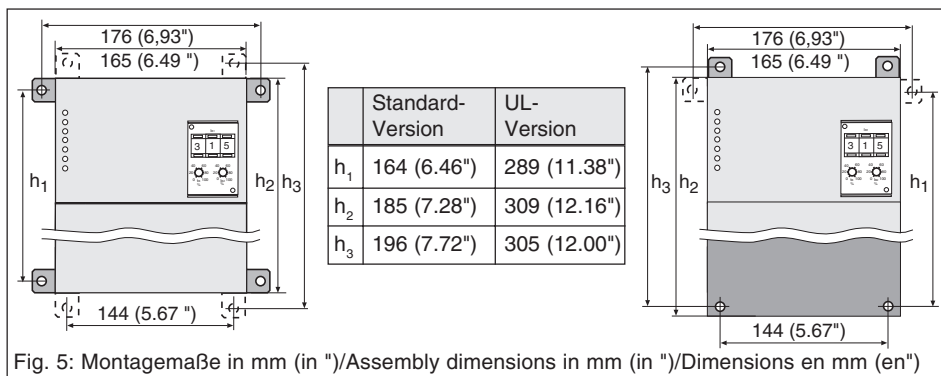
Montagemaße in mm (in ")/Assembly dimensions in mm (in ")/Dimensions en mm (en")
